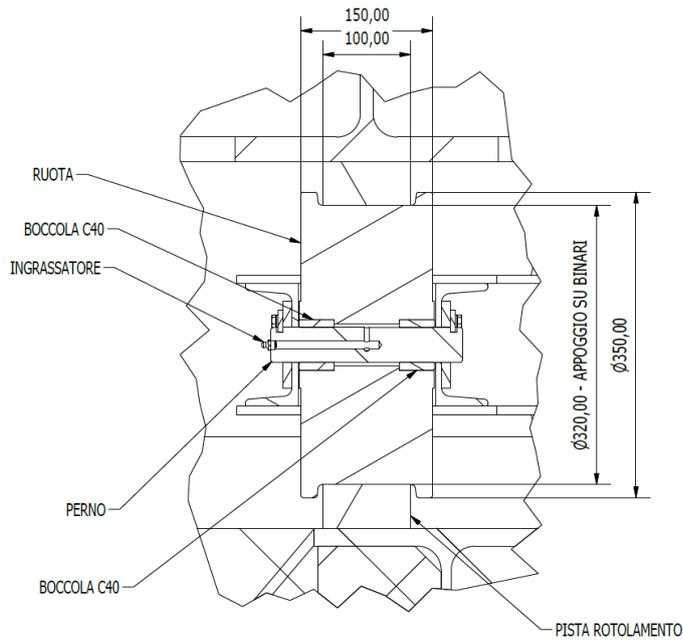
vista in sezione della ruota, delle boccole, del perno e del telaio dodecagonale
